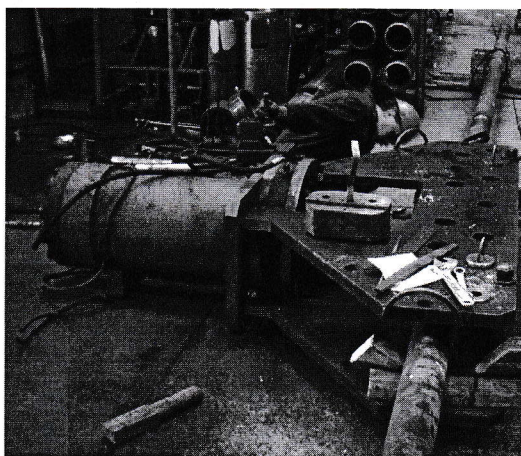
Правка трубогибом сплошной заготовки для изготовления трубы $\phi 146 \times 43 \times 10000$ мм глубоким сверлением
